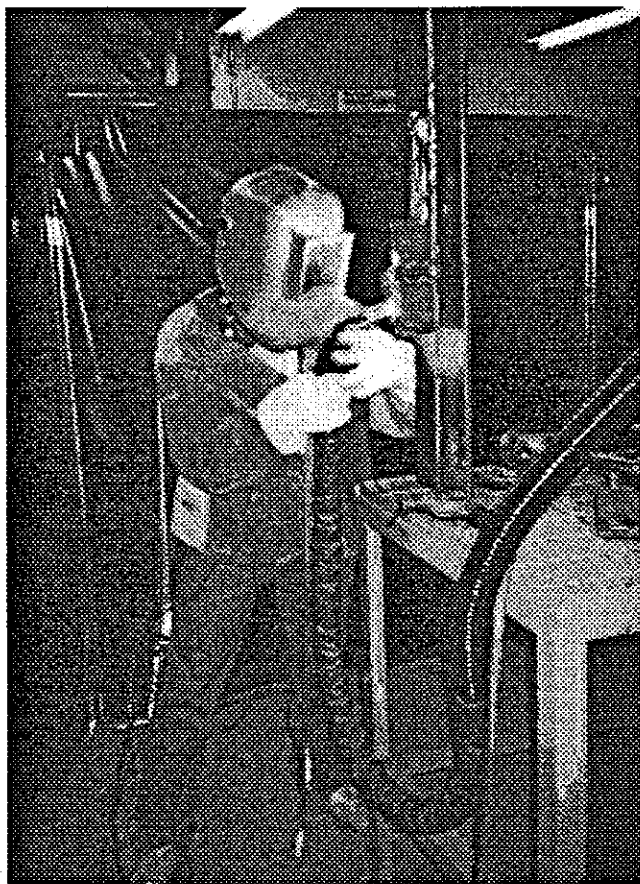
Soudeur réalisant une soudure dans la position 3G.
